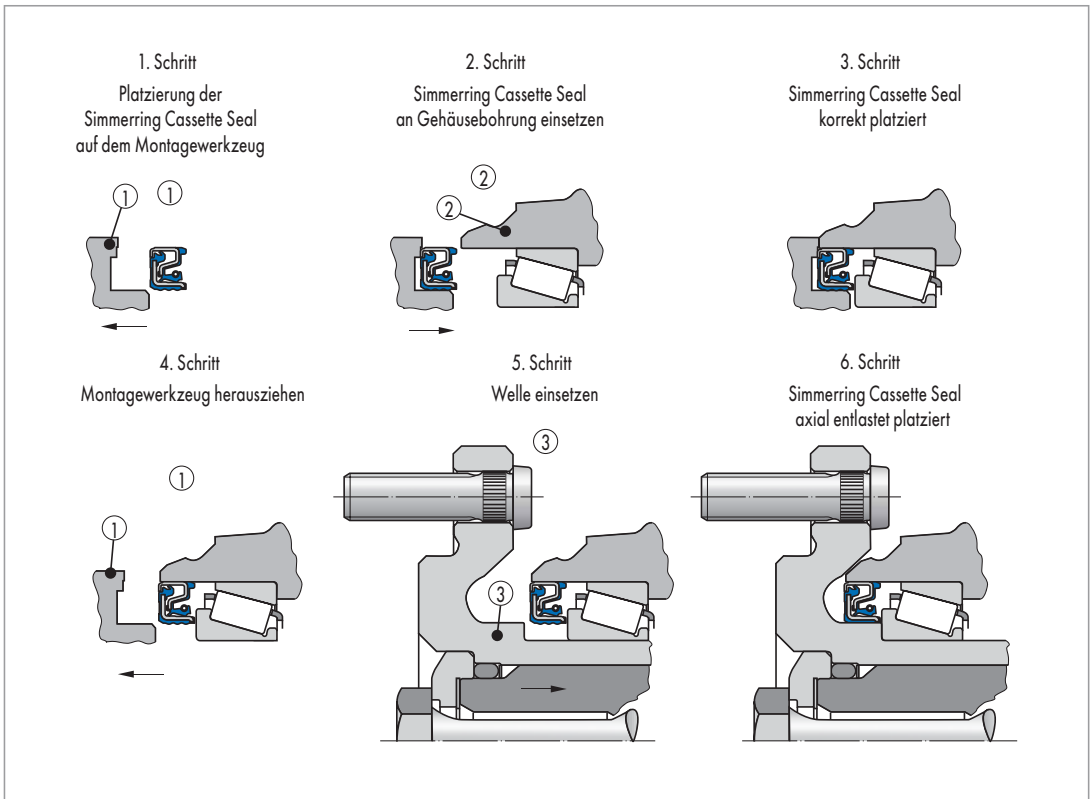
Montage von Simmerring Cassette Seal – Fall A (mit „bearing stop“)
